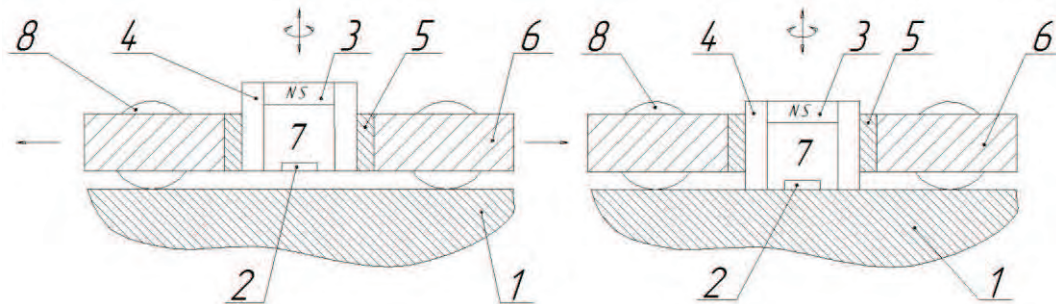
ЭМА преобразователь для контроля объектов с неравномерным покрытием 1 – объект контроля; 2 – плоский проводниковый излучатель; 3 – магнит; 4 – магнитопровод; 5 – механизм движения преобразователя; 6 – платформ; 7 – преобразователь; 8 – механизм движения платформы
